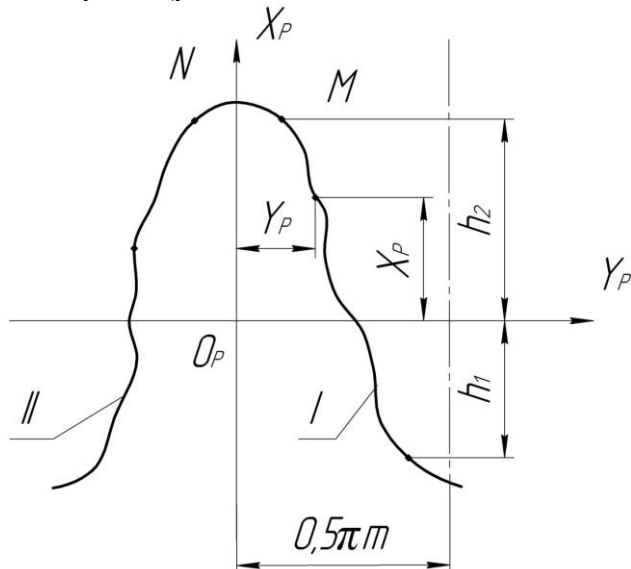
Обобщенный исходный контур зубьев колеса
